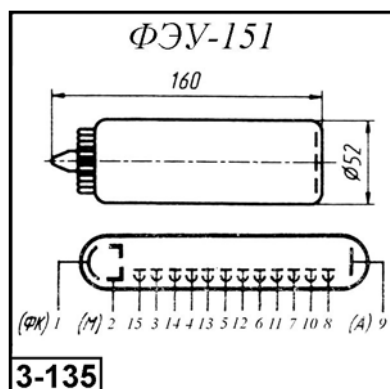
Внешний вид, габаритные размеры, схемы расположения штырьков, порядок их соединения с электродами фотумножителя ФЭУ-151
